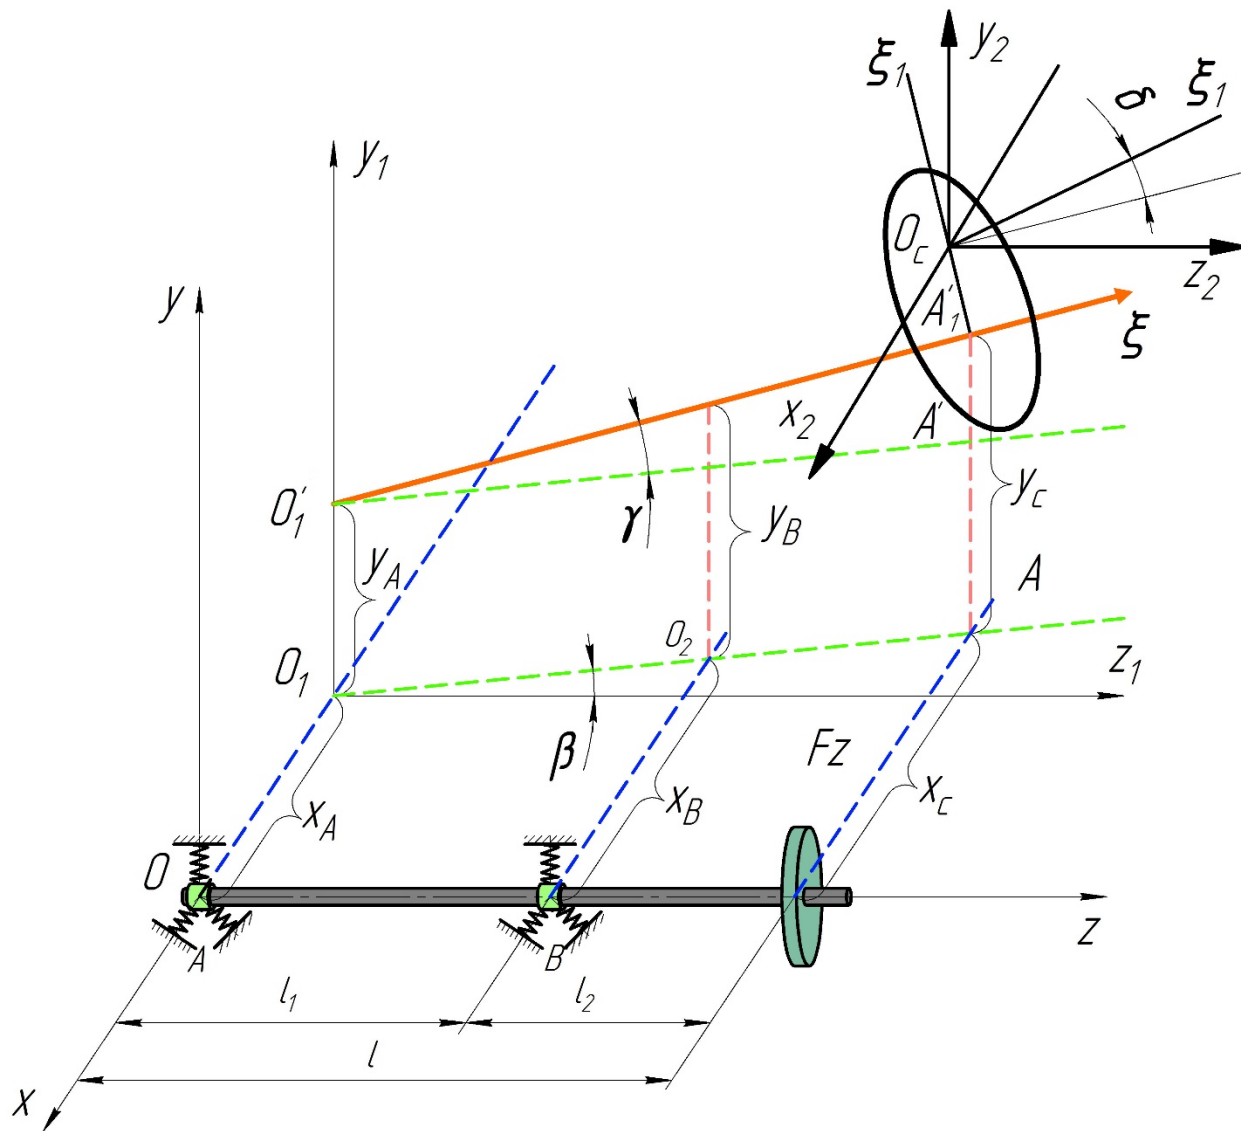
Схема розташування шпинделя в нерухомій системі координат  $xuz$
